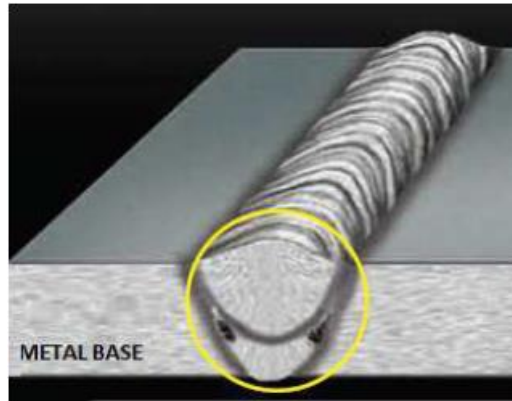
Inclusiones de escoria en la soldadura [4].
